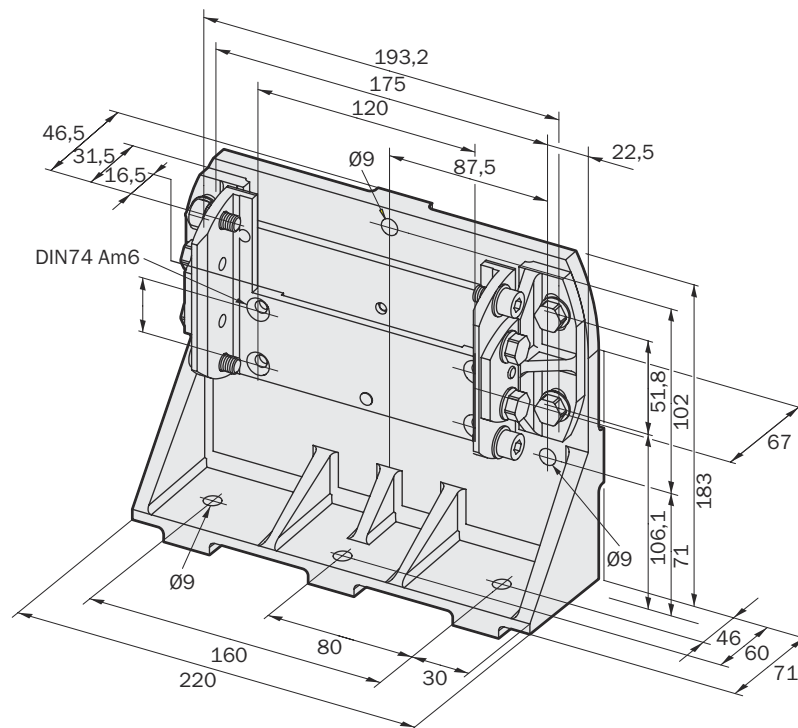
Plan côté kits de fixation 1, 2 et 3 (mm)
